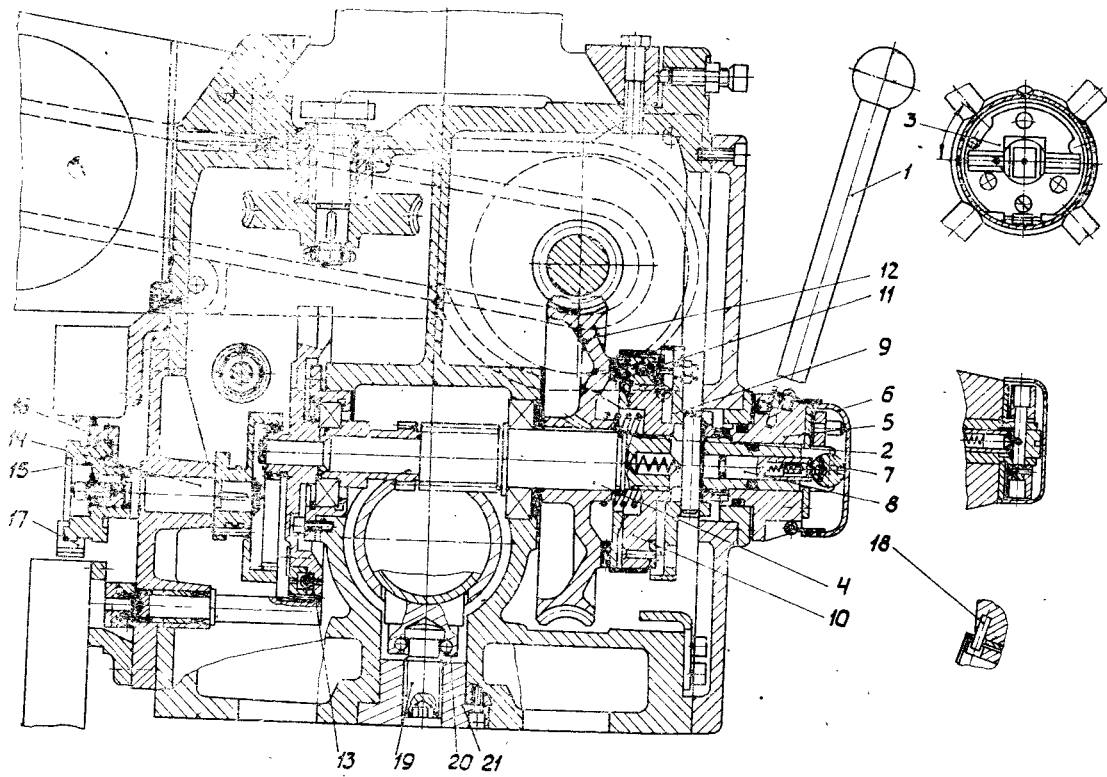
Сверлильная головка станка 2С132ПФ2И.
